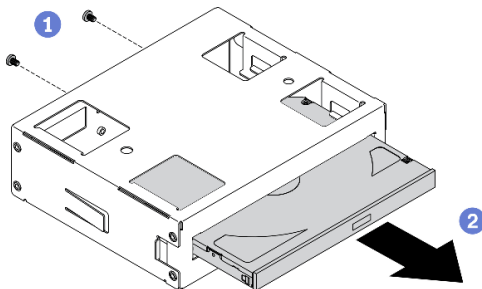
Entfernen des flachen optischen Laufwerks aus dem Laufwerkpositionsadapter
